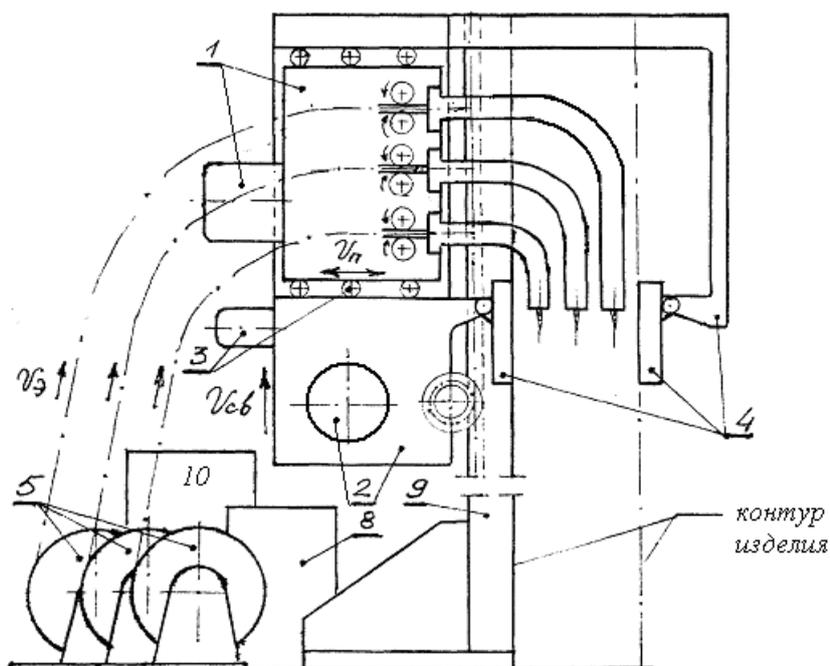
Конструктивная схема автомата для электрошлаковой сварки включает:
